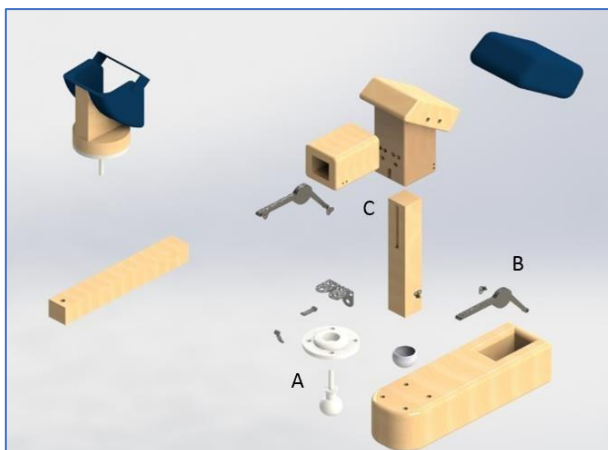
Vista explosionada modulo 2. Fuente: Autora.
